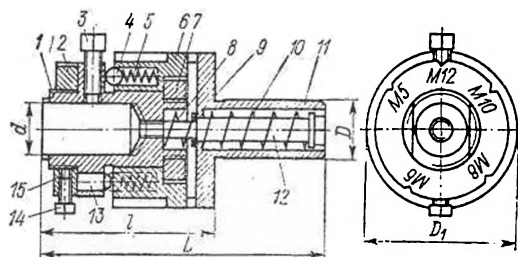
Запобіжний різьбонарізний патрон
